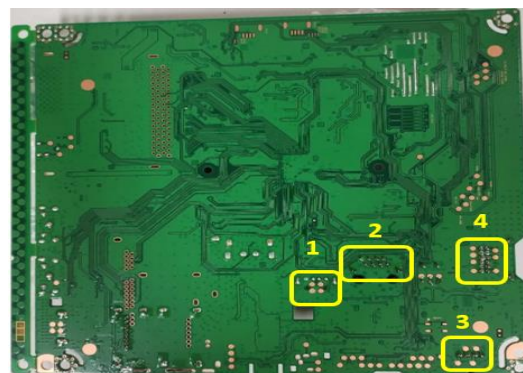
Visão Inferior da PCBA: Solda em 4 áreas específicas da PCBA.
